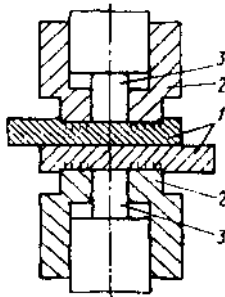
Схема сварки с предварительным зажатием свариваемых деталей.
